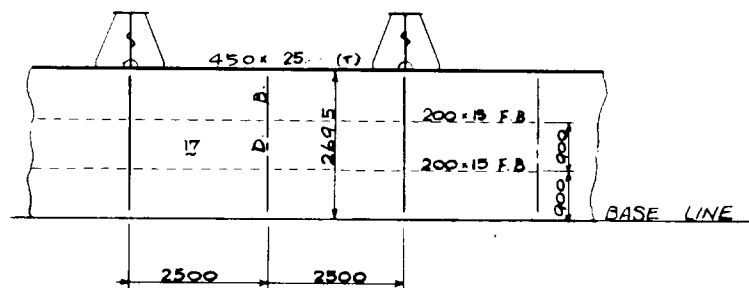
1. 2. 3 BOTTOM CENTER LINE GIRDER
